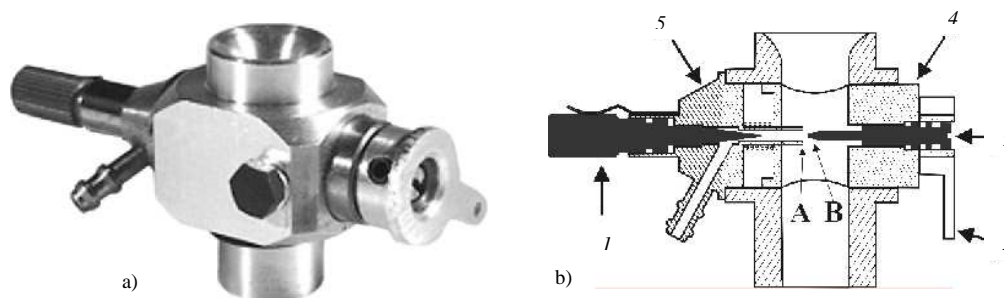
a) Carburador del Motor. b) Dibujo esquemático y partes del carburador donde 1 es la Aguja de alta, 2 es la Aguja de ralentí, 3 es el Brazo del acelerador, 4 es el Barril del acelerador y 5 es el Tubo atomizador.
